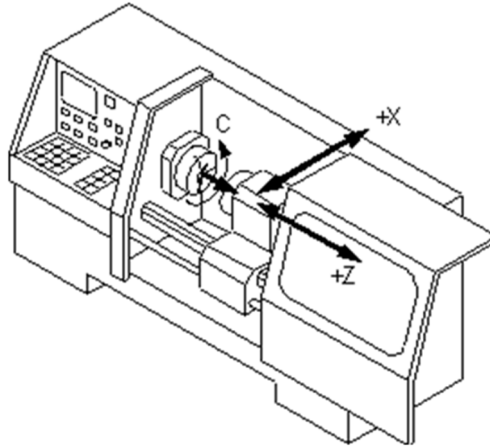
Система координат токарного верстата з можливістю додаткового обертання шпинделя навколо осі Z
